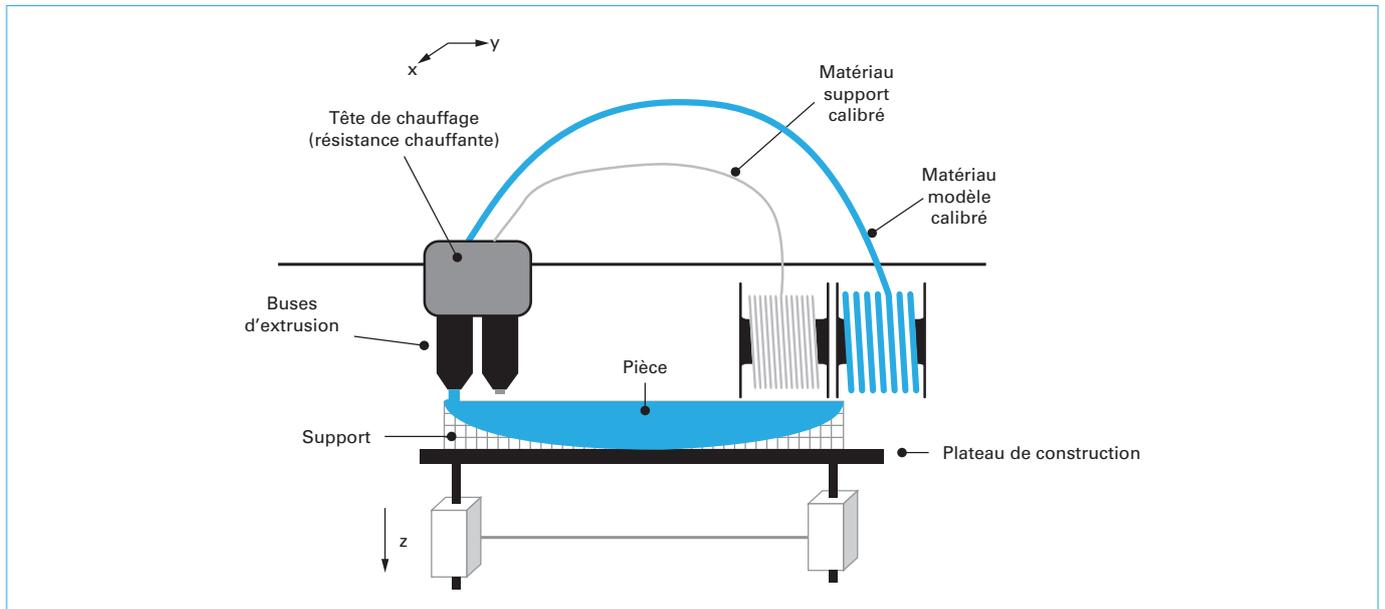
Illustration du procédé d'extrusion de matière – Cas d'une machine à deux buses, adapté de Rias [12]
